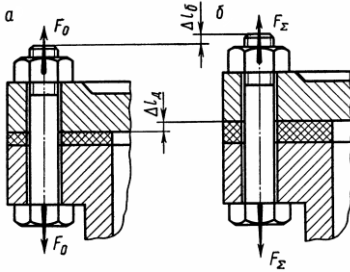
К расчету болтов с внешней нагрузкой, раскрывающей стык
